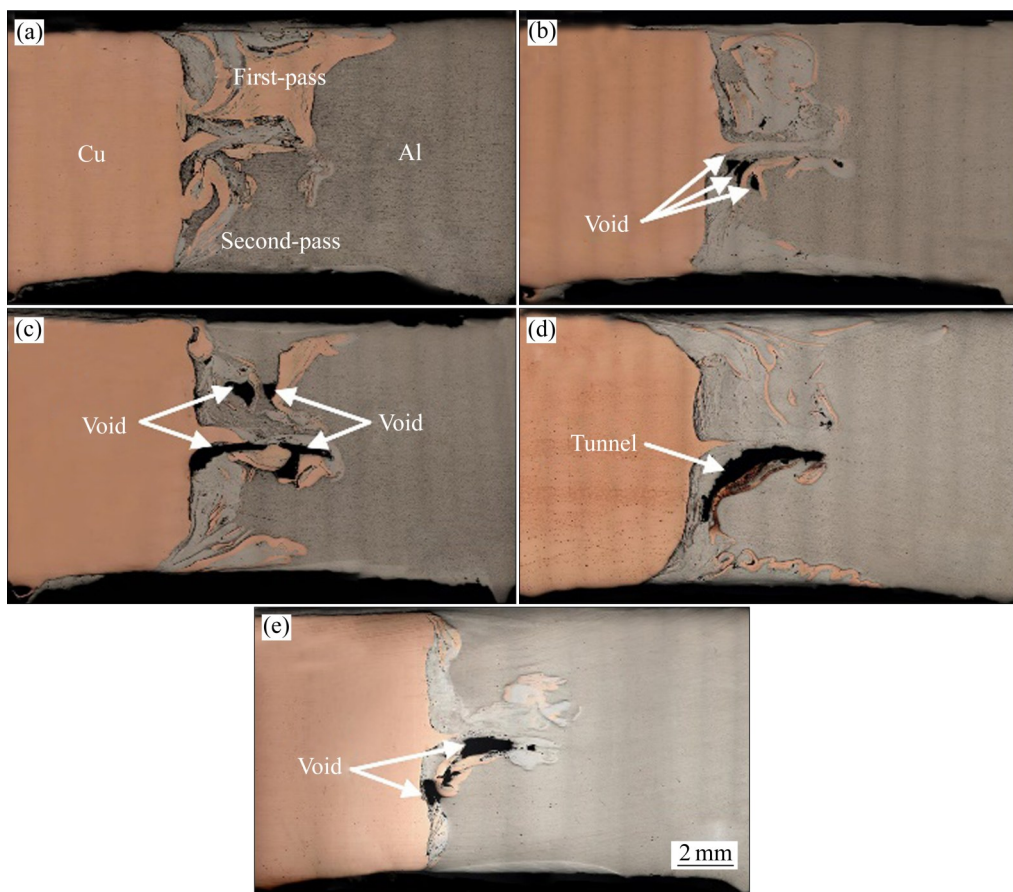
不同焊接速度条件下 Al/Cu 双面 FSW 焊缝横断面宏观形貌
